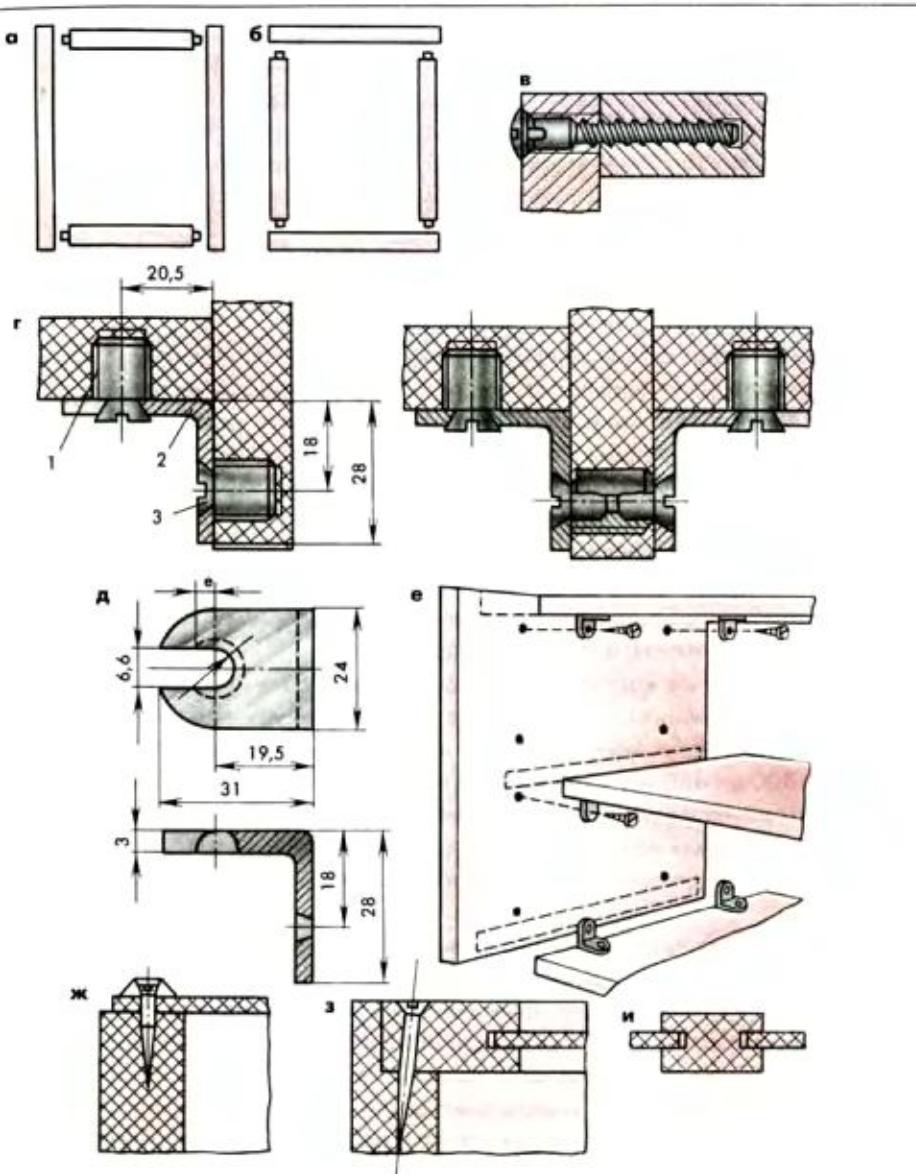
Схемы расположения стенок корпуса и соединения стенок:
